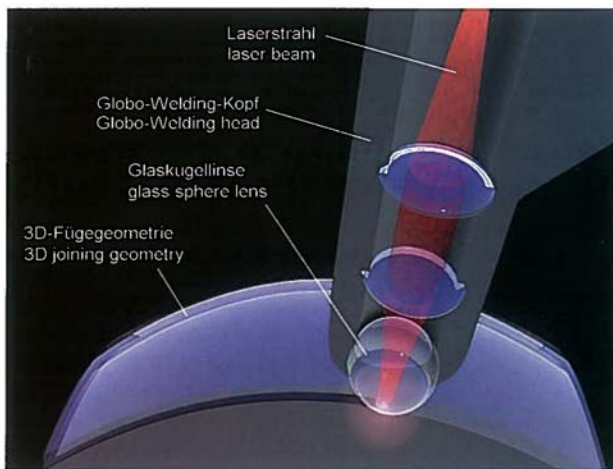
Prinzip des Laserstrahlschweißens
